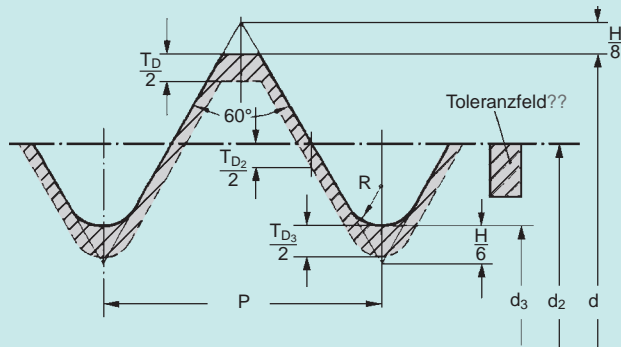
Bolzengewinde mit Grundabmaß 0 (Toleranzlage h)
